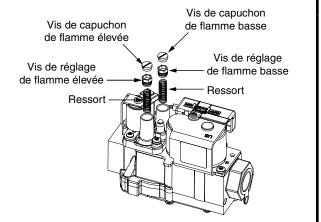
Démontage du ressort et de la vis de réglage du régulateur
